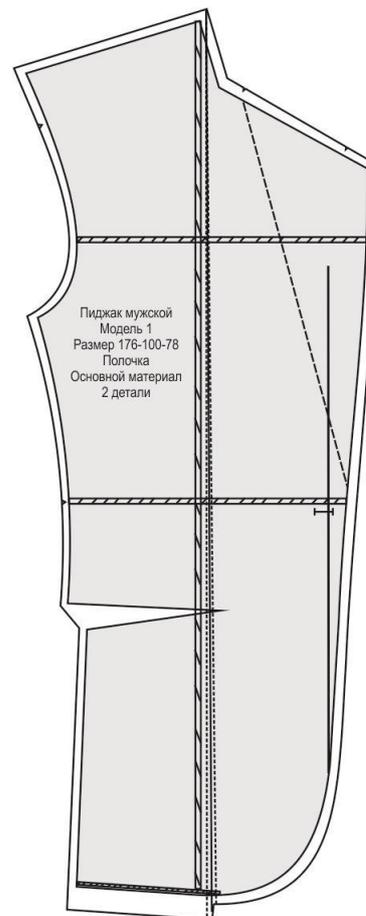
Пример основного лекала детали полочки мужского пиджака
